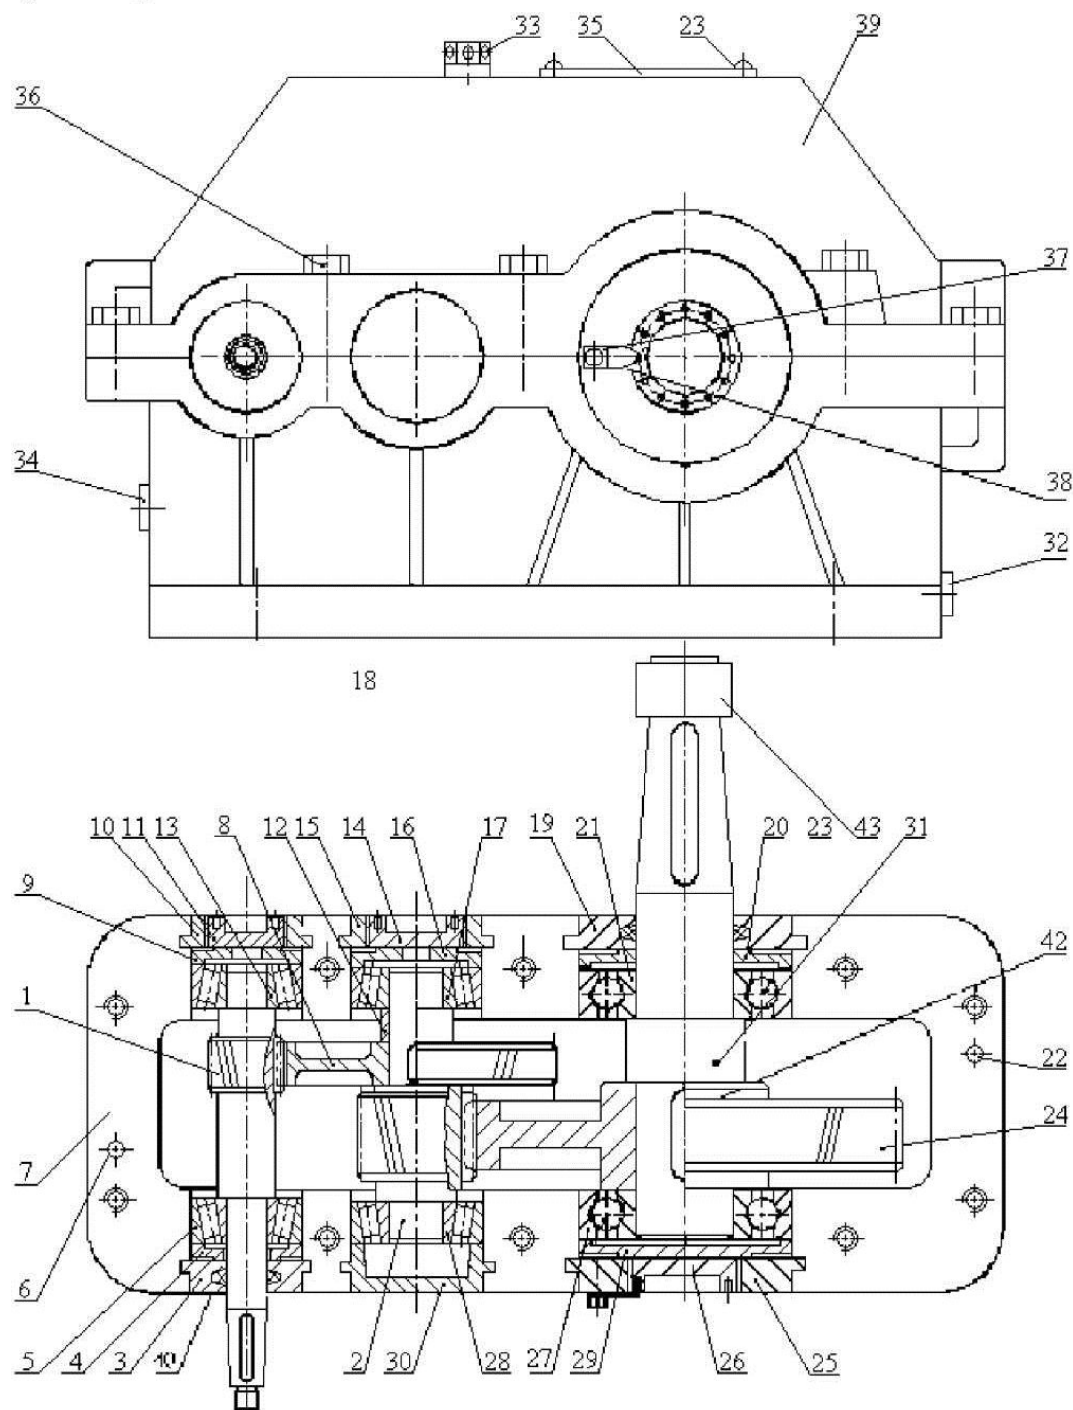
Двухступенчатый зубчатый цилиндрический редуктор
